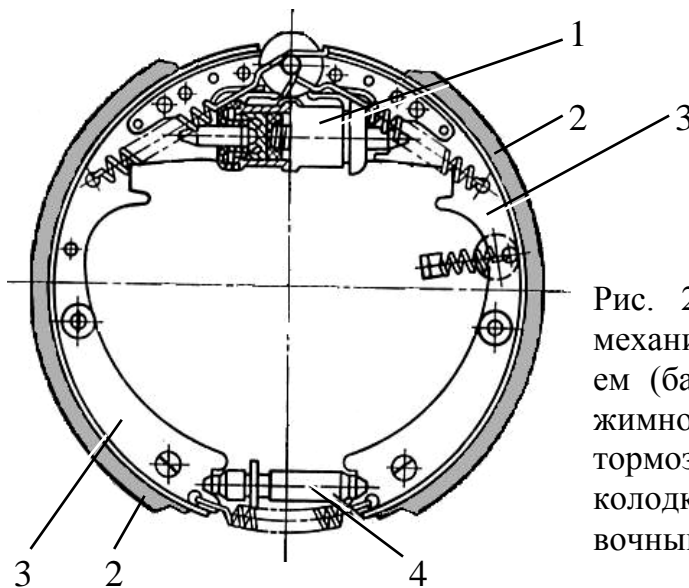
Барабанный тормозной механизм с большим самоусилением (барабан не показан): 1 – разжимное устройство; 2 – накладки тормозных колодок; 3 – тормозные колодки; 4 – толкатель с регулировочным устройством
